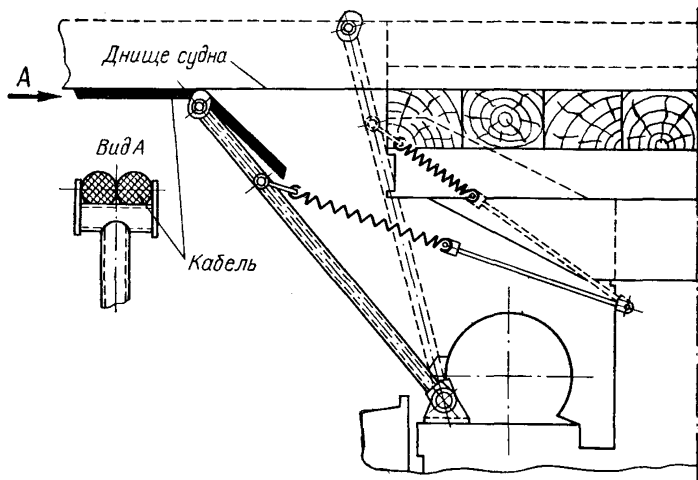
Схема подвески кабелей с помощью пружинного приспособления
